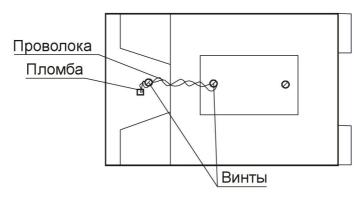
Схема пломбировки вторичного преобразователя при креплении на DIN-рейку.
